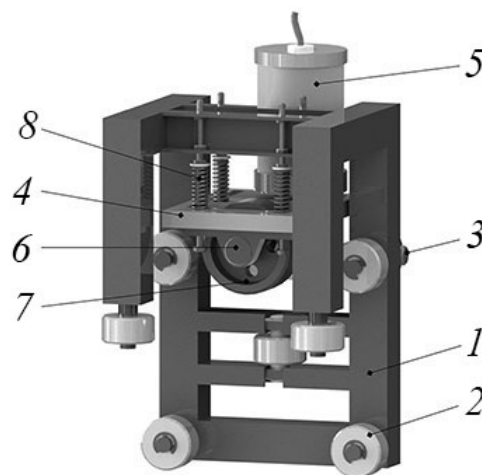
Общий вид приводной подвески: 1 – металлоконструкция несущей секции; 2 – роlikи; 3 – ось для крепления к ленте; 4 – металлоконструкция прижимной секции; 5 – мотор-редуктор; 6 – подшипниковая опора; 7 – приводной ролик; 8 – прижимное устройство.
